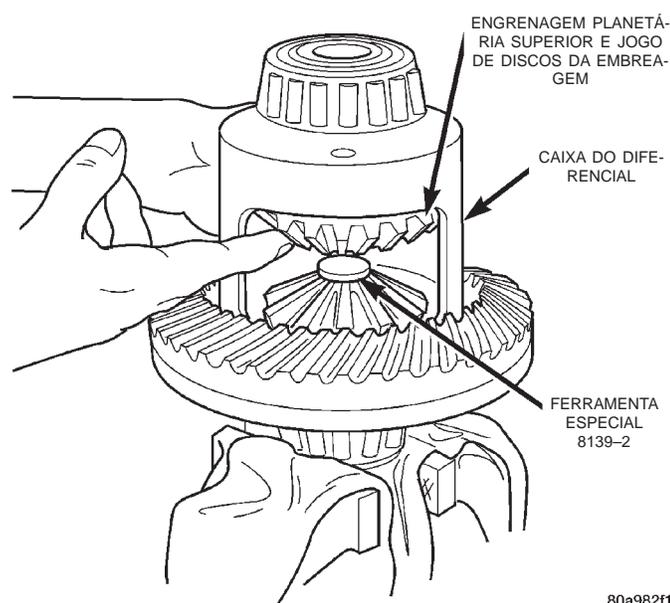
Engrenagem Planetária Superior e Instalação do Jogo de Discos da Embreagem
